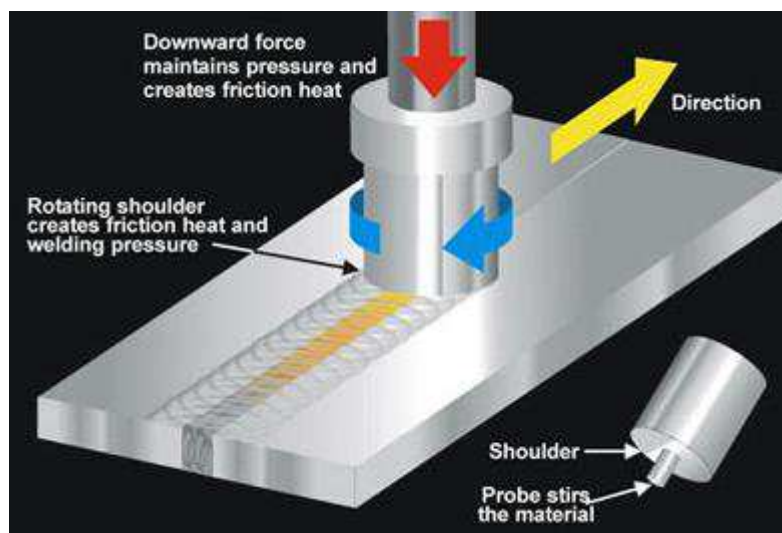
Ilustração do processo de soldagem FSW (ESAB, 2016).
